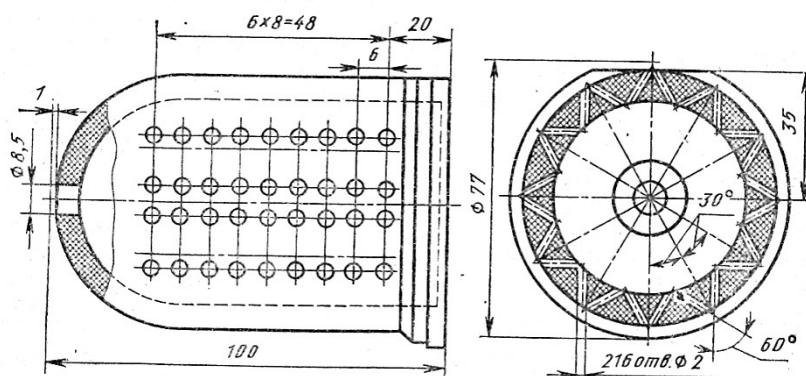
Глушитель шума пневмопереключателя фрикционной муфты сцепления и тормоза прессов
